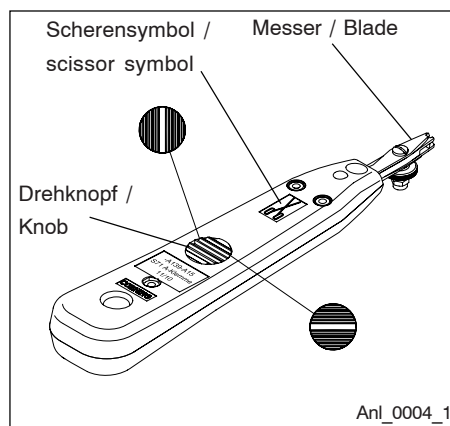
Anlegewerkzeug mit grauer Griffschale / Fig. 2: Tool with grey handle
